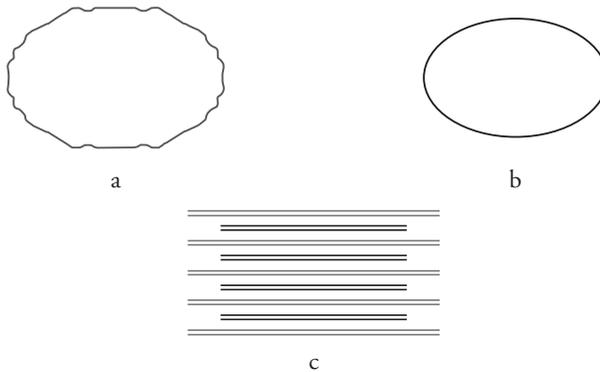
Composition d'une série de fonds de plateaux à laminier :
